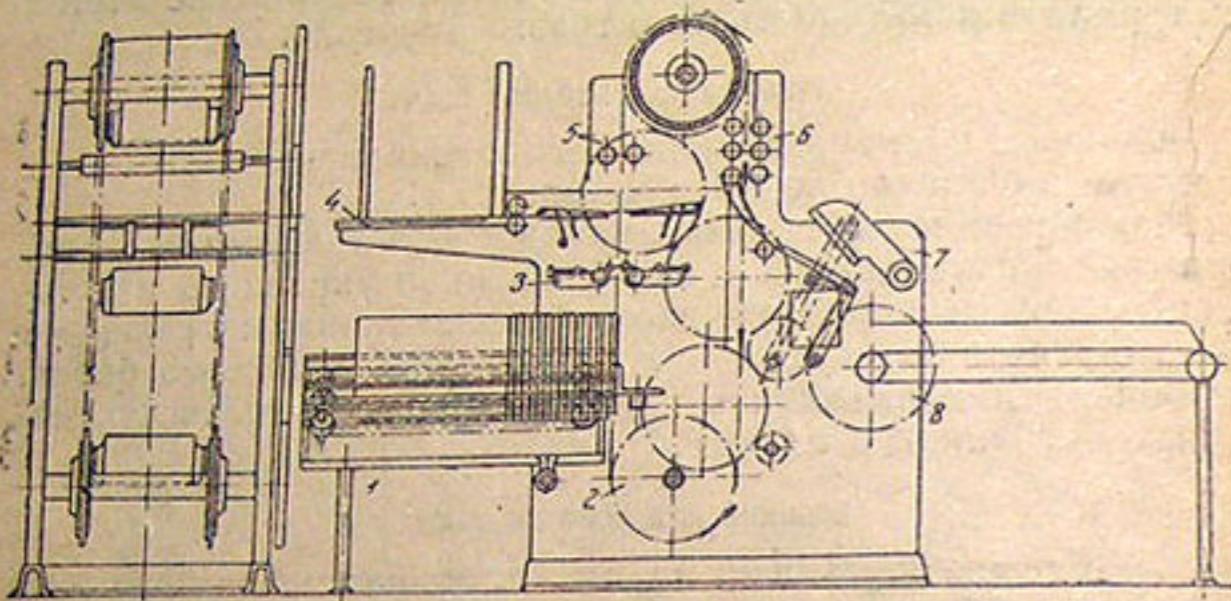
Книгоставочная машина НИИ НКМП РСФСР: 1 — транспортер для подачи книг; 2 — цепной транспортер для книг; 3 — kleemazательный аппарат; 4 — устройство для подачи крышек; 5 — валики для предварительной обжимки; 6 — устройство для съемки книг с крыльев; 7 — пресс; 8 — транспортер для вставленных книг.
